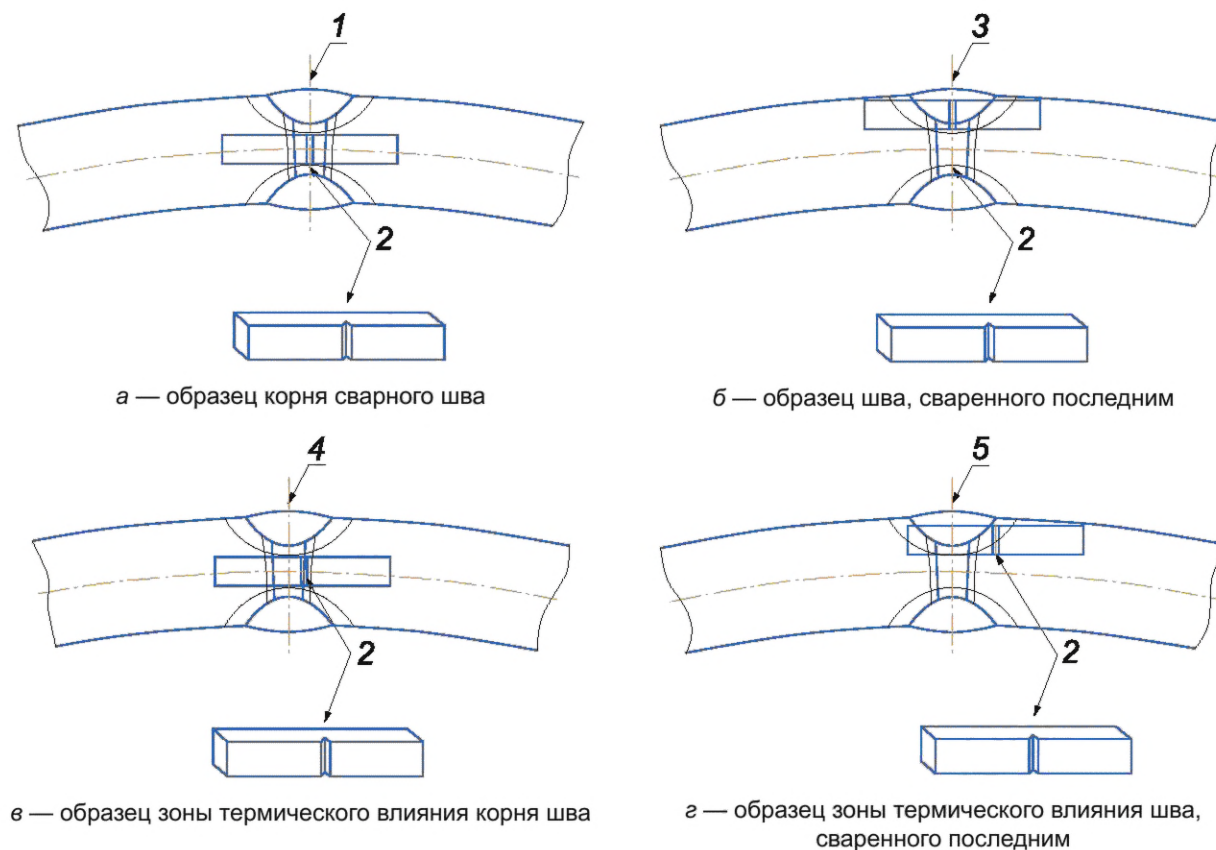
Расположение образцов для испытаний на ударный изгиб труб ДСФ
